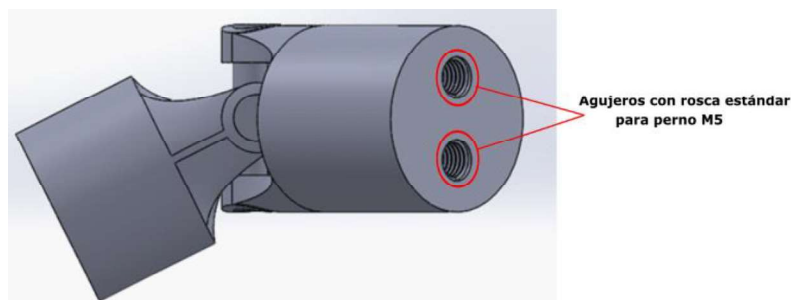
Dibujo 3D en SolidWorks de junta universal Belden maquinada.
